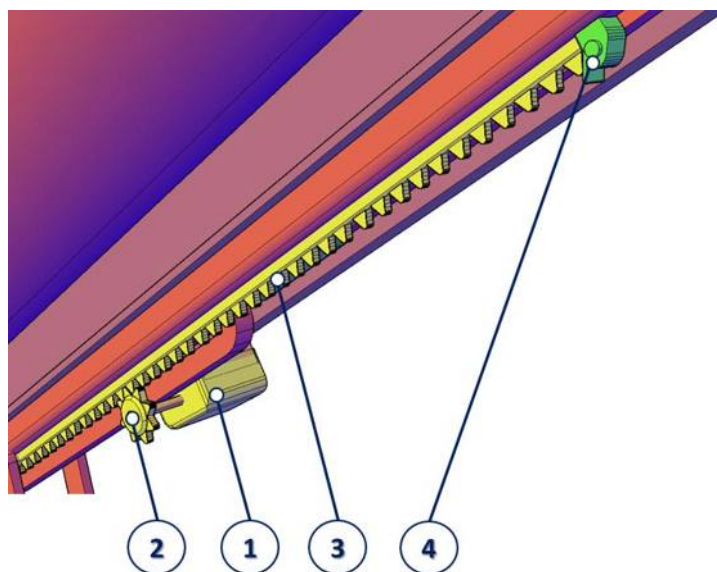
Конструкция привода: 1 - мотор-редуктор; 2 - зубчатое колесо; 3 - зубчатая рейка; 4 - переключатель концевой
